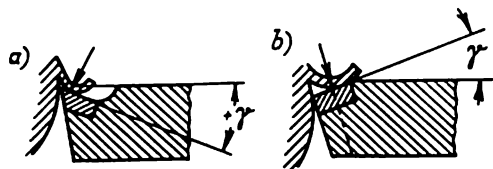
Conditions de travail d'un outil à plaquette rapportée en carbure métallique
